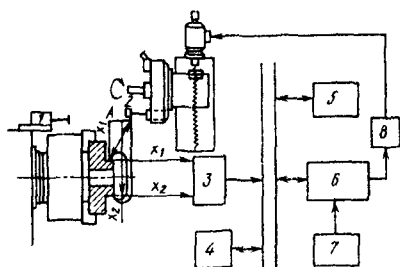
Схема измерения диаметра обрабатываемых заготовок на токарном станке с ЧПУ
